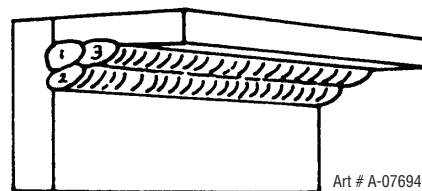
Posición elevada, soldadura de ángulo
